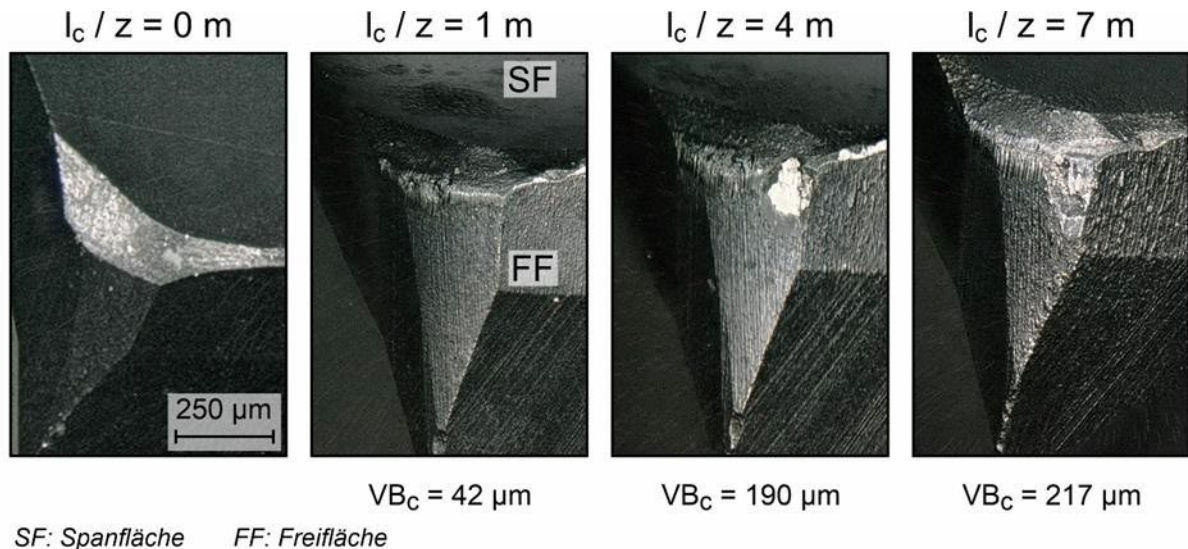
REM-Aufnahmen eines geschliffenen Voll-PcBN –Torusfräsers
